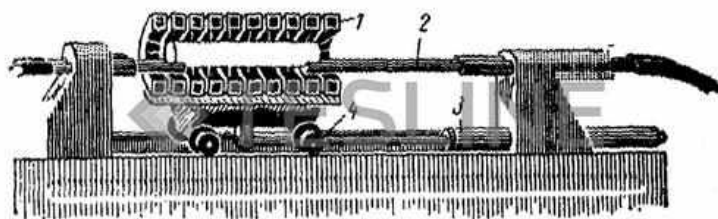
Схема периодического нагревателя с подвижным индуктором:
